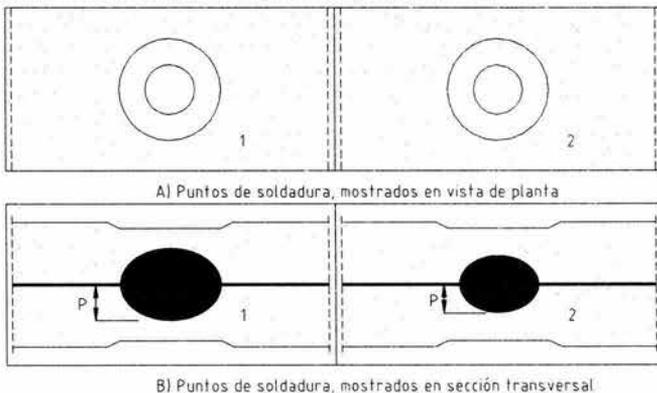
(A) Apariencia de superficie de 2 puntos sucesivos de soldadura de 1 mm. de espesor en cada lámina.
